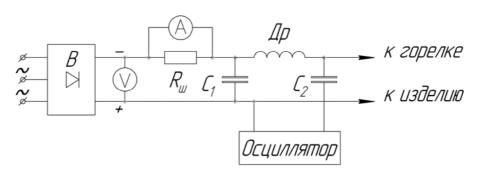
Принципиальная схема устройства сварочного аппарата для аргонодуговой сварки
